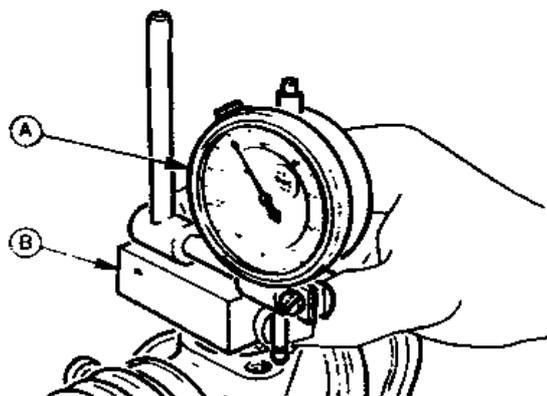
Определение толщины пакета шайб для регулировки демпфера рейки (Разд.35)
